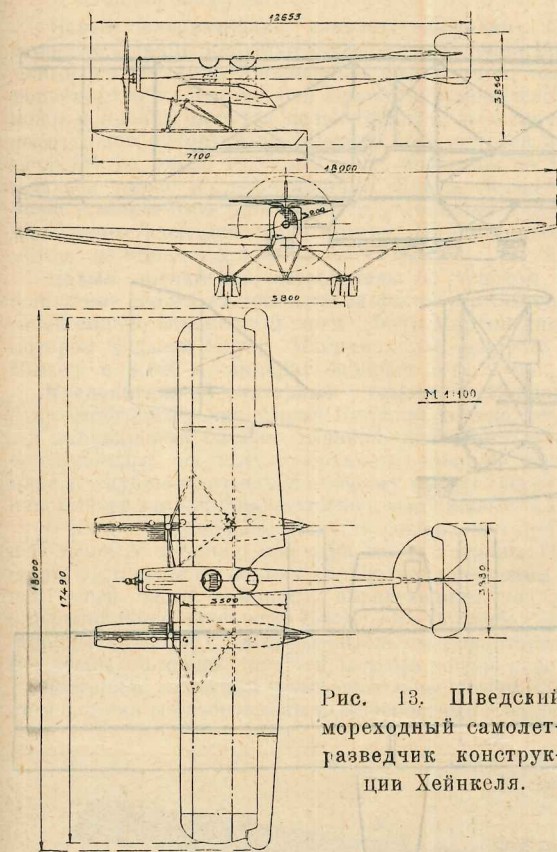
Шведский мореходный самолет-разведчик конструкции Хейнкеля.
